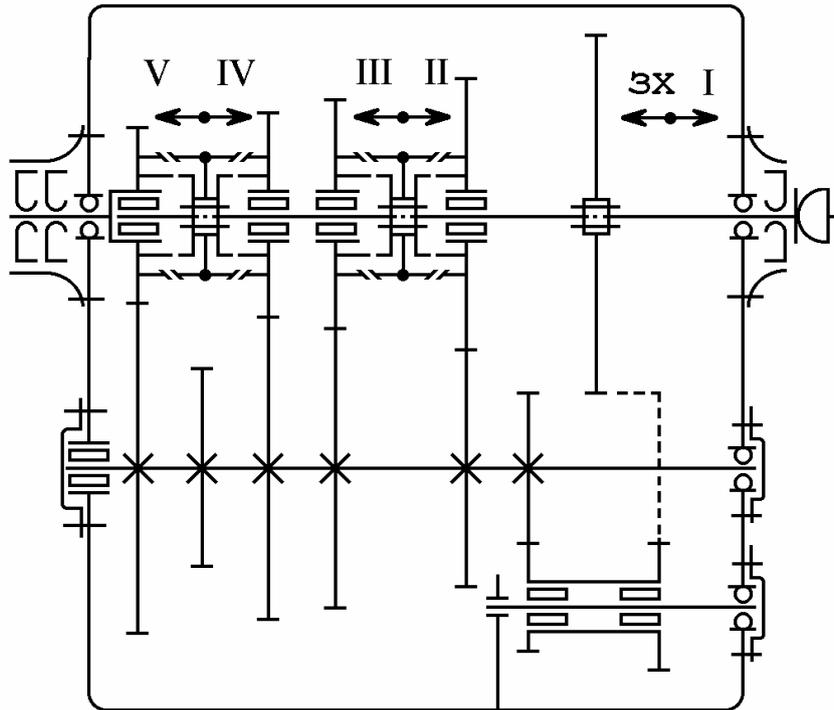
Автомобильная 5-ступенчатая коробка передач
